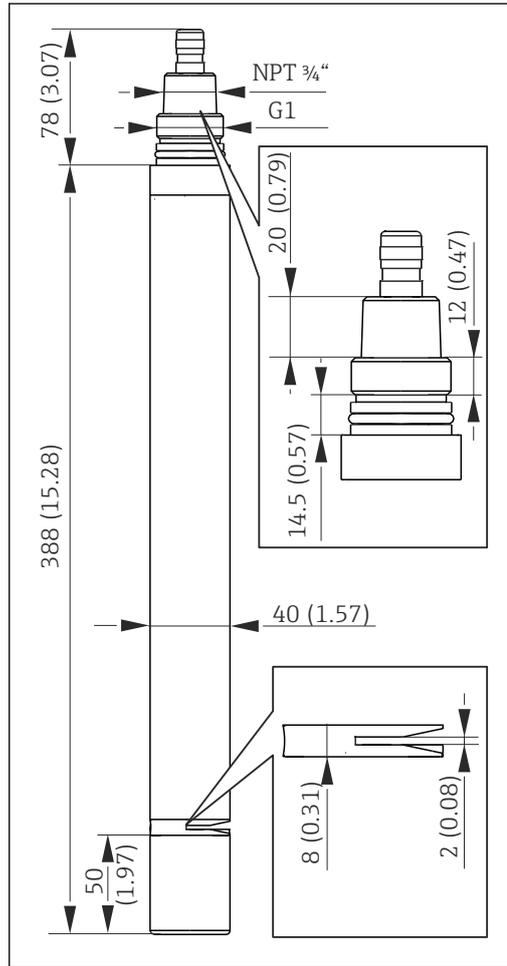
2 mm (0.08 in) 光程的传感器的外形尺寸示意图; 单位: mm (in)
